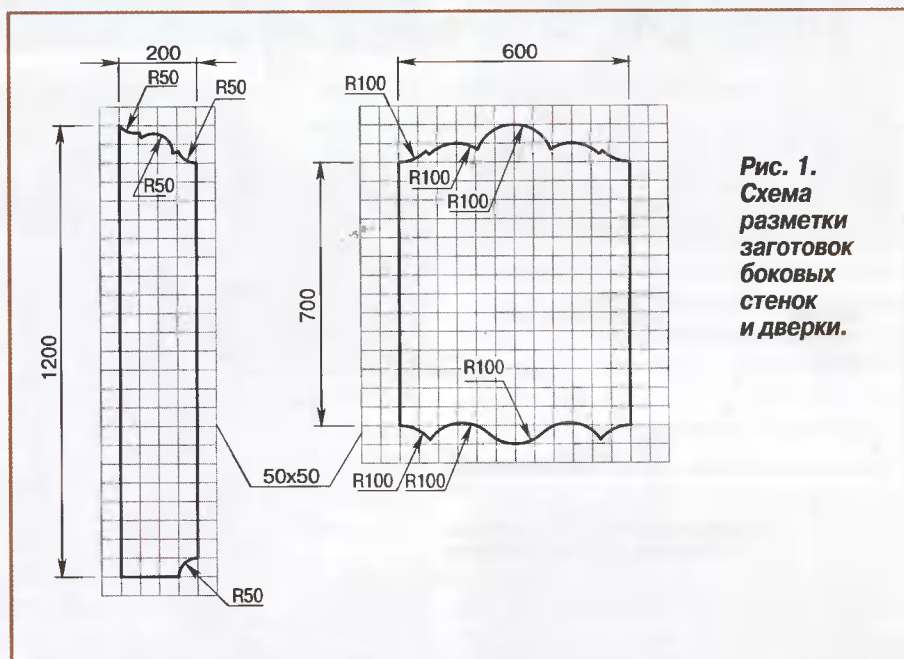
Схема разметки заготовок боковых стенок и дверки.
